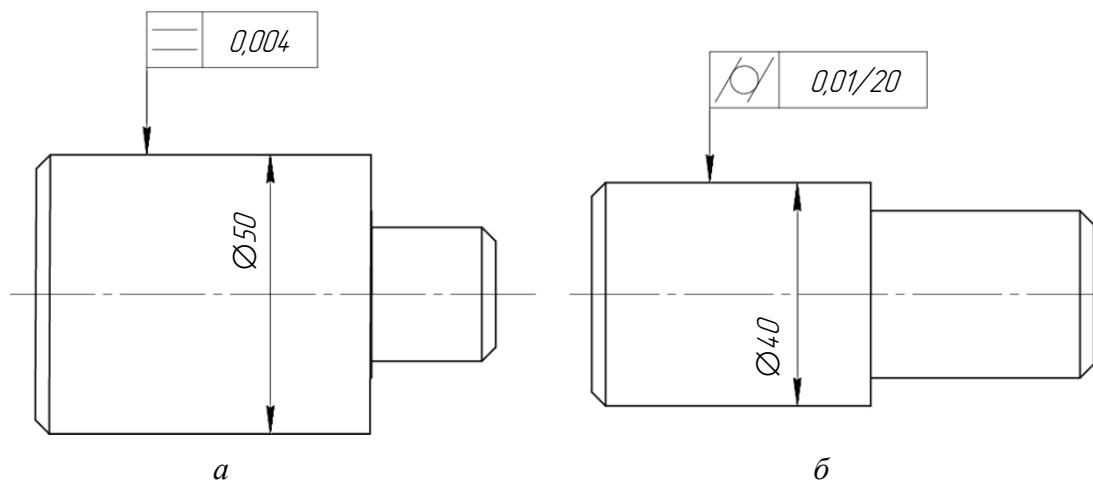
Примеры обозначения допусков формы:
